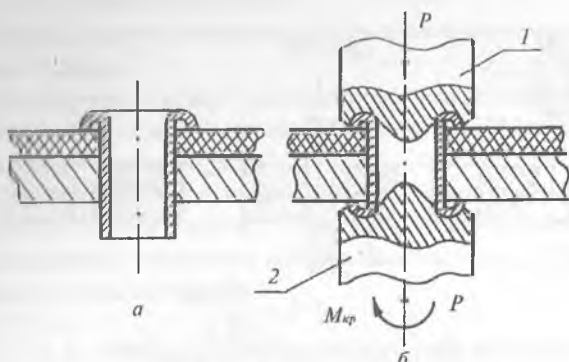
Трубчатая заклепка: а — конструкция заклепки; б — образование замыкающей головки (раскатка); 1 — опорный элемент раскатного оборудования; 2 — раскатник
